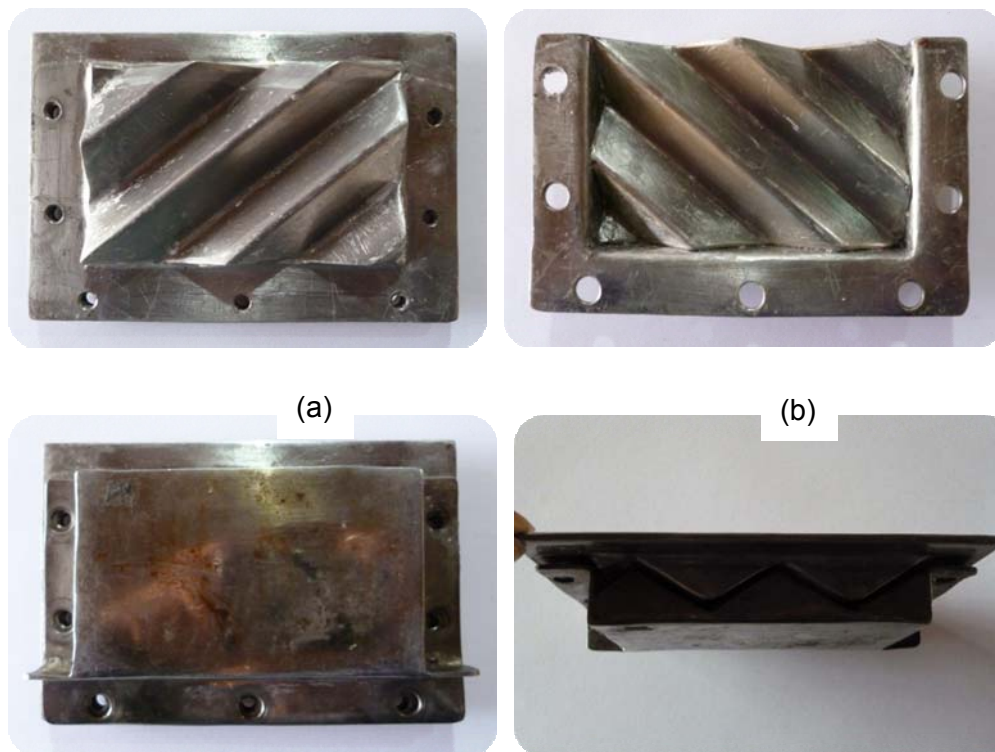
Molde para polimerización fabricado en acero inoxidable (a) Lámina corrugada (macho), (b) Lámina corrugada (hembra), (c) Vista frontal molde, (d) Vista lateral molde
